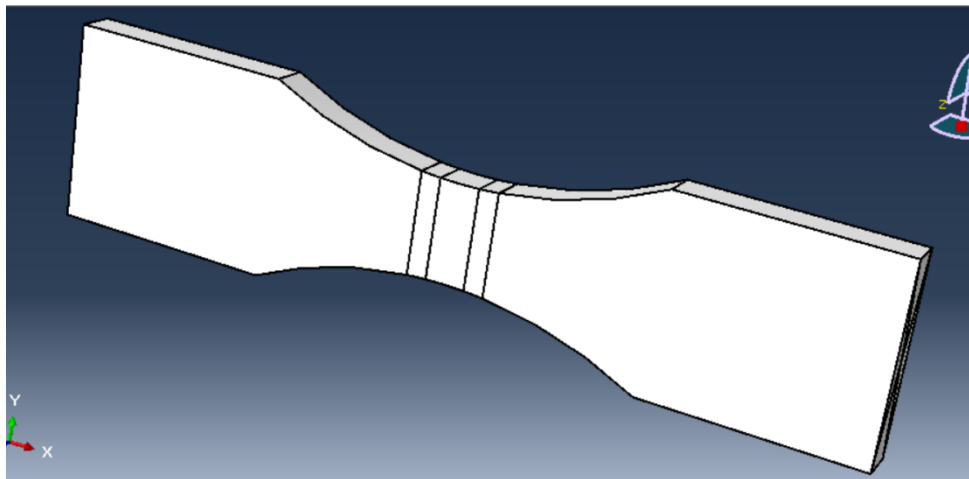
L'éprouvette modélisée avec ABAQUS avec soudage.
